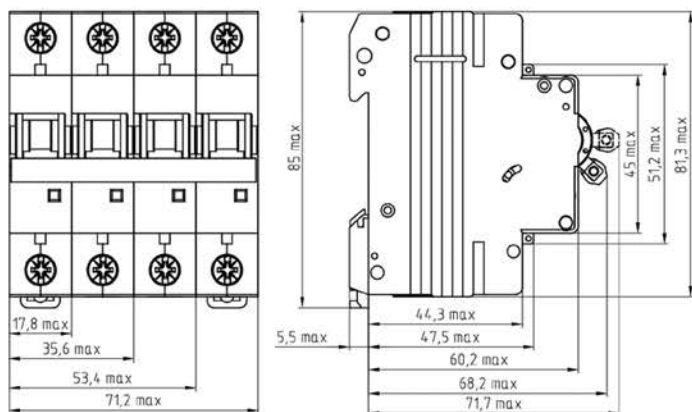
Габаритные, установочные и присоединительные размеры выключателей:
